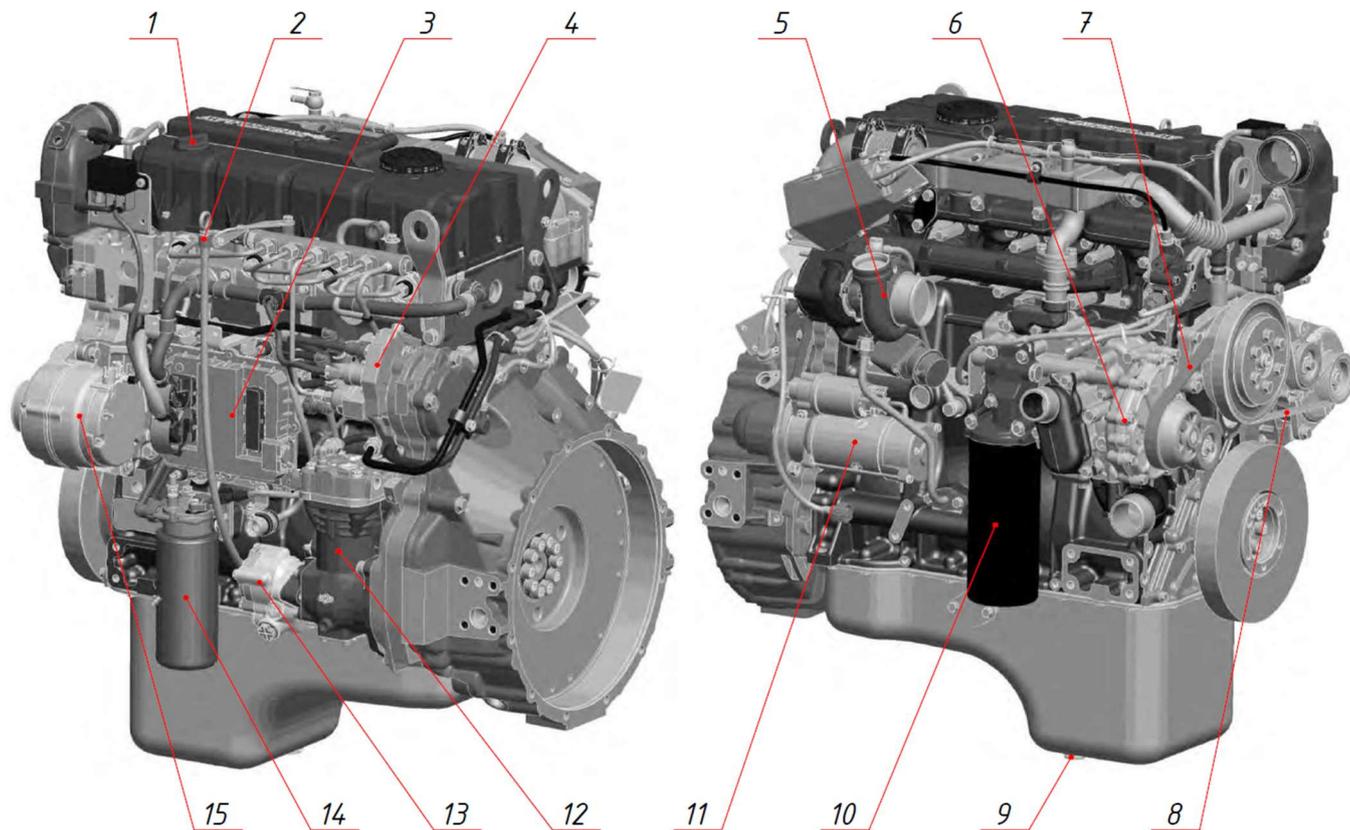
Расположение агрегатов и узлов двигателя ЯМЗ-53422
